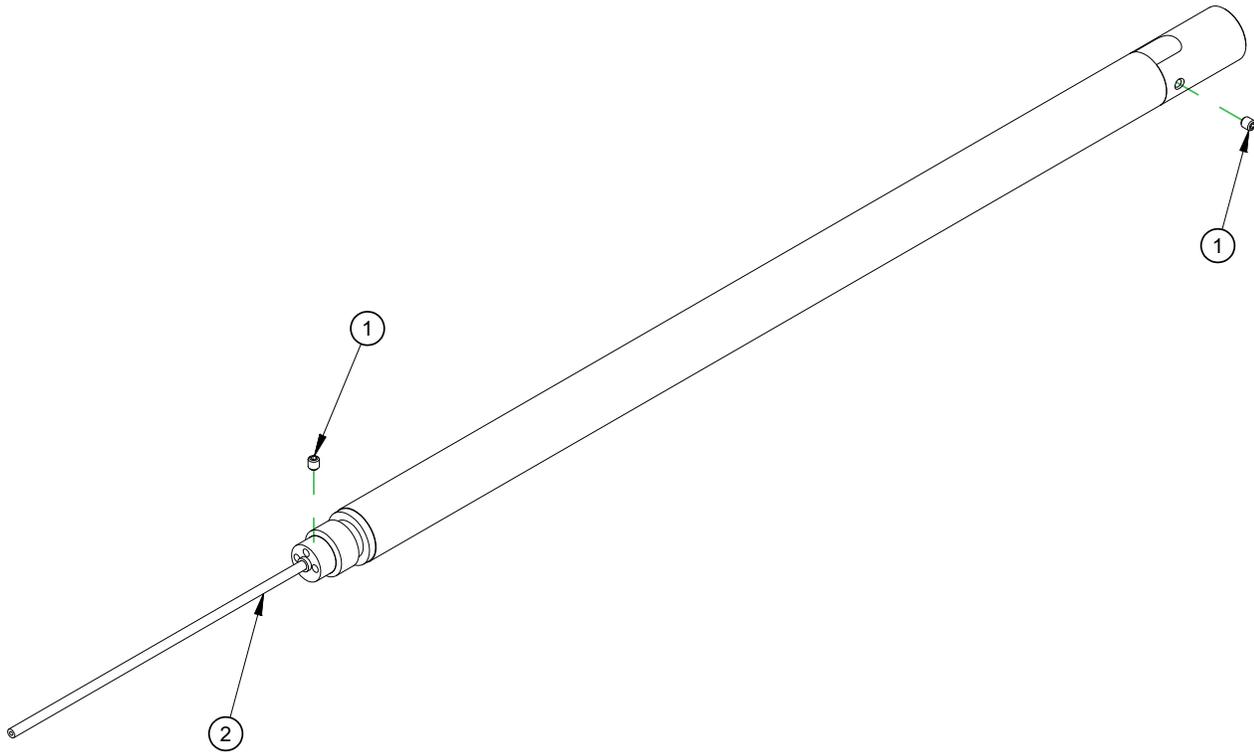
ENSEMBLE DE MONTAGE DE SUPPORT DE TORCHE (RÉF. 70132)
